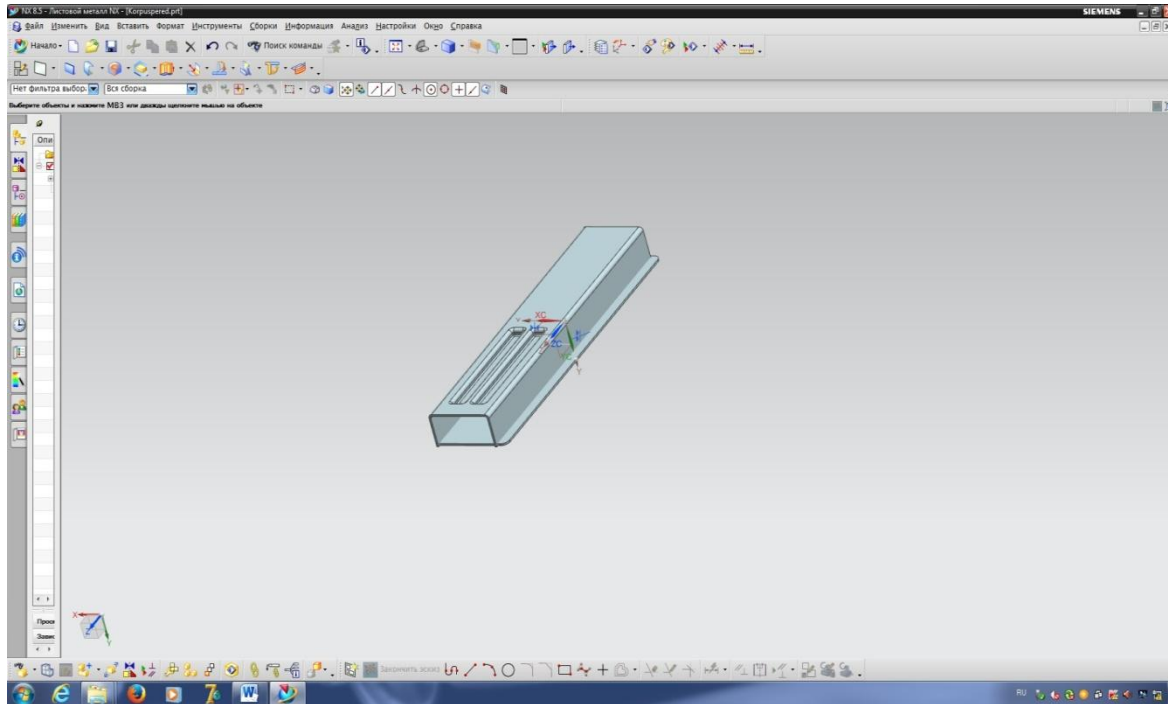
Сборка «корпус» и «лист передний и задний».
